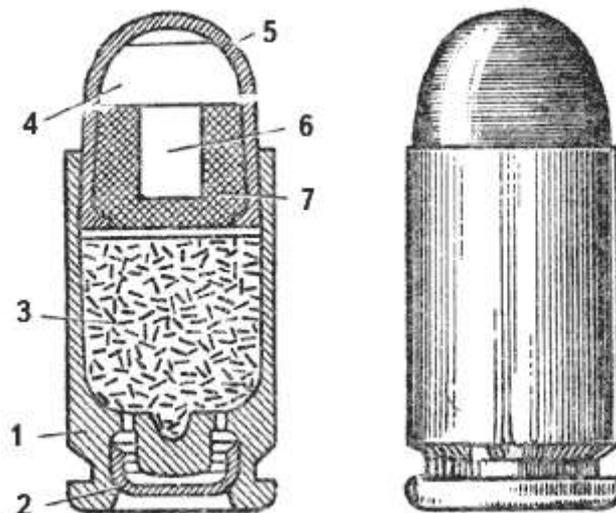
Общий вид 9-мм пистолетного патрона и его устройство:
